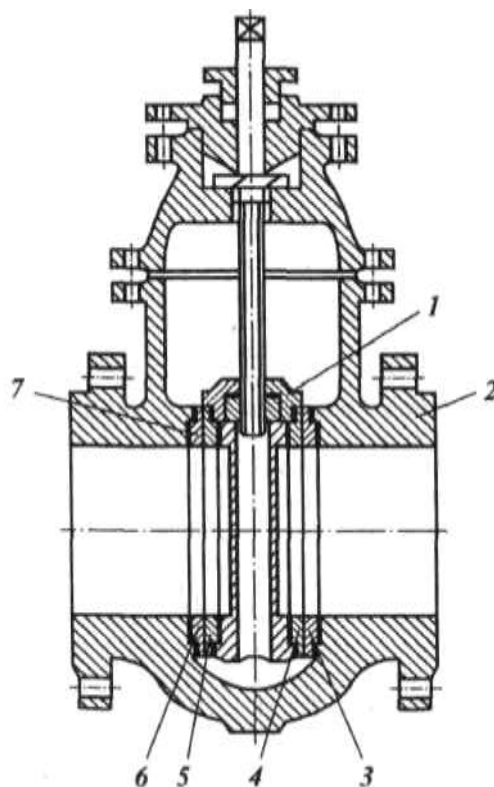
Ремонт корпусу і клина засувки способом додаткових ремонтних деталей із застосуванням клейового з'єднання: 1 - клин; 2 - корпус;
